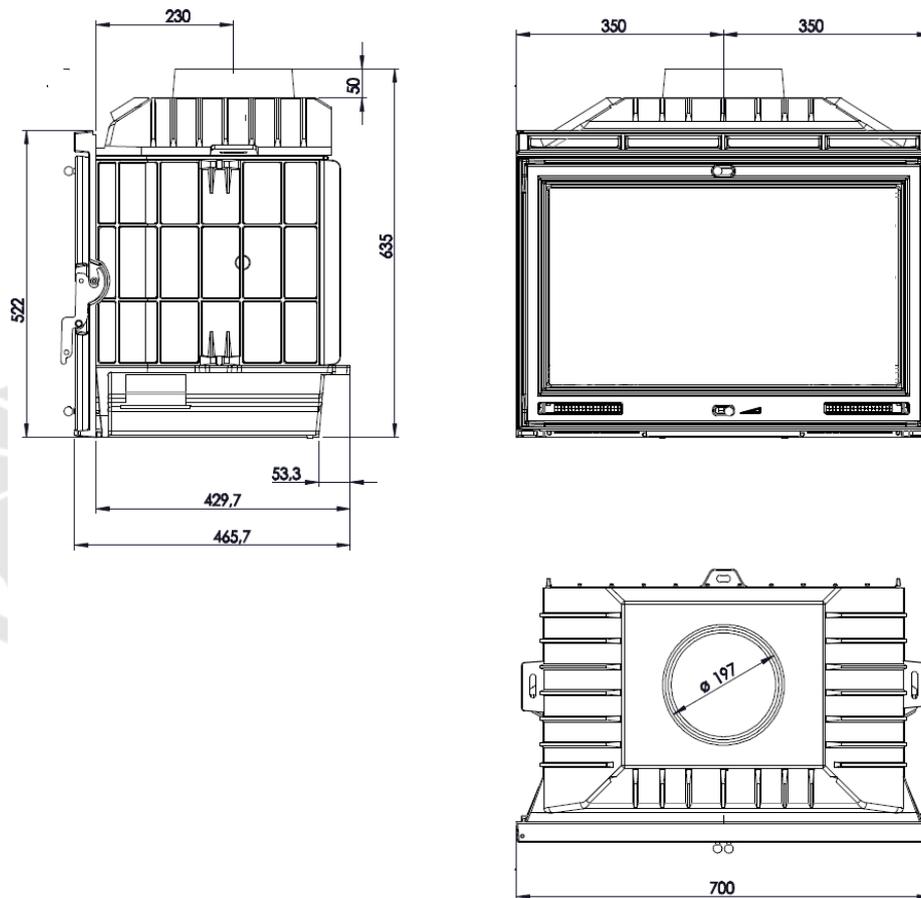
Dimensiones en mm de la chimenea RE-700
